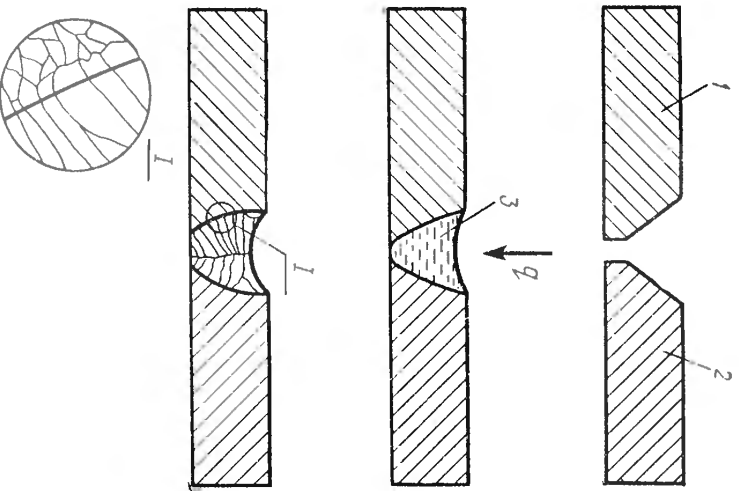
Схема образования соседних при сварке плавлением: 1, 2 — свариваемые заготовки, 3 — ванна жидкого металла;  $l$  — макроструктура зерен на границе шва
